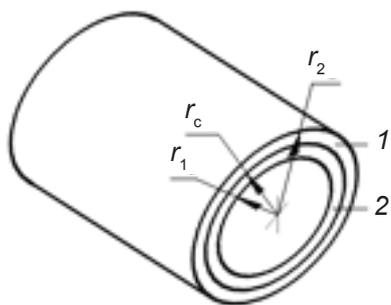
Схема цилиндрической комбинированной отливки: 1 – отливка; 2 – керамическая вставка
